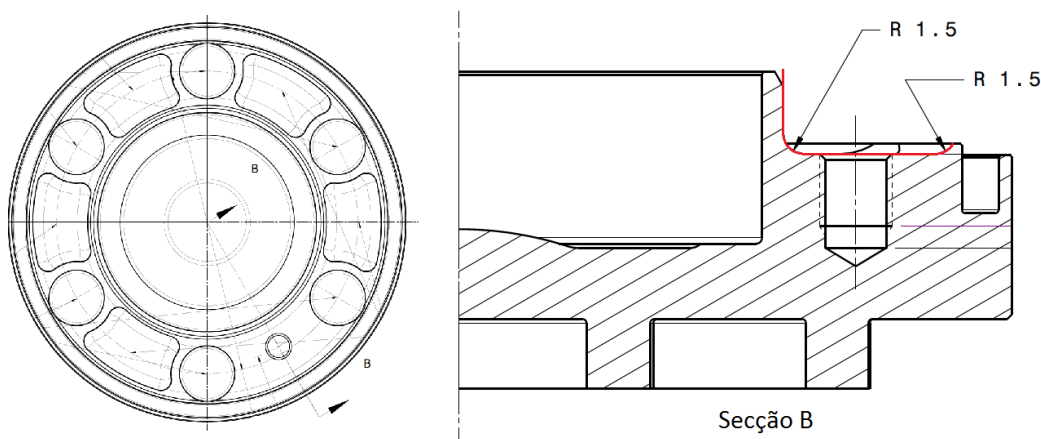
Superfície a maquinar na 7ª Operação.
